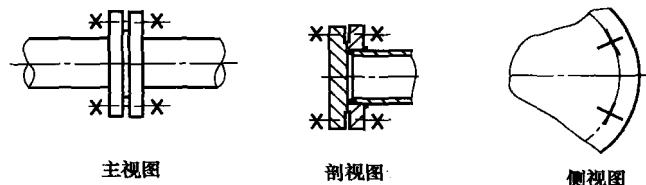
装配图中一般法兰的连接螺栓、螺母、垫片的简化画法
